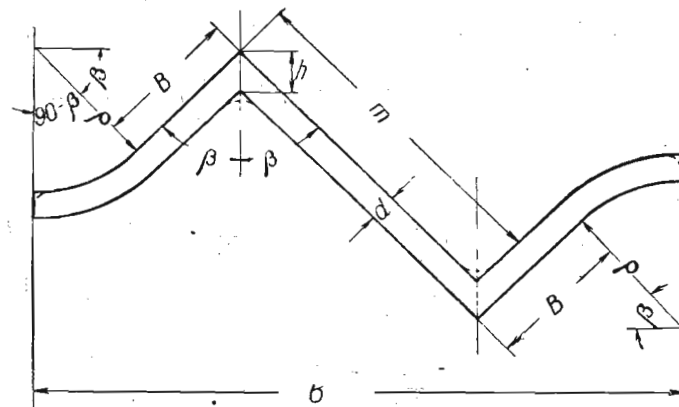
Схема калибра зетового профиля к выводу геометрических соотношений в калибре для прокатки зетовой стали
